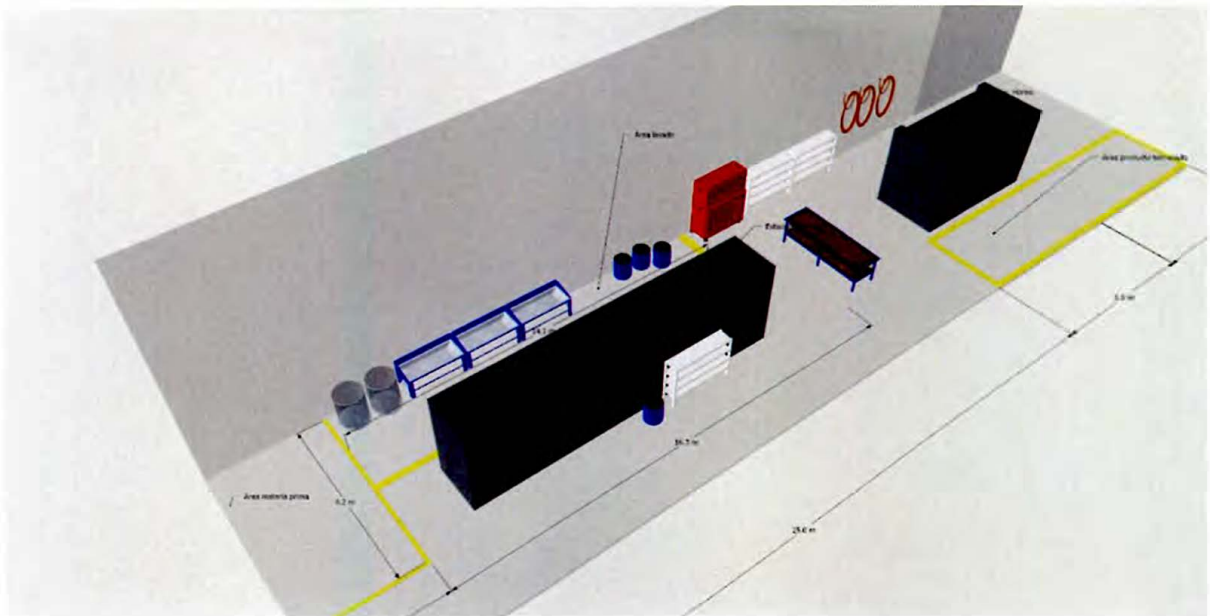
Propuesta de diseño de la estación de trabajo de soldadura implementando 5s.
